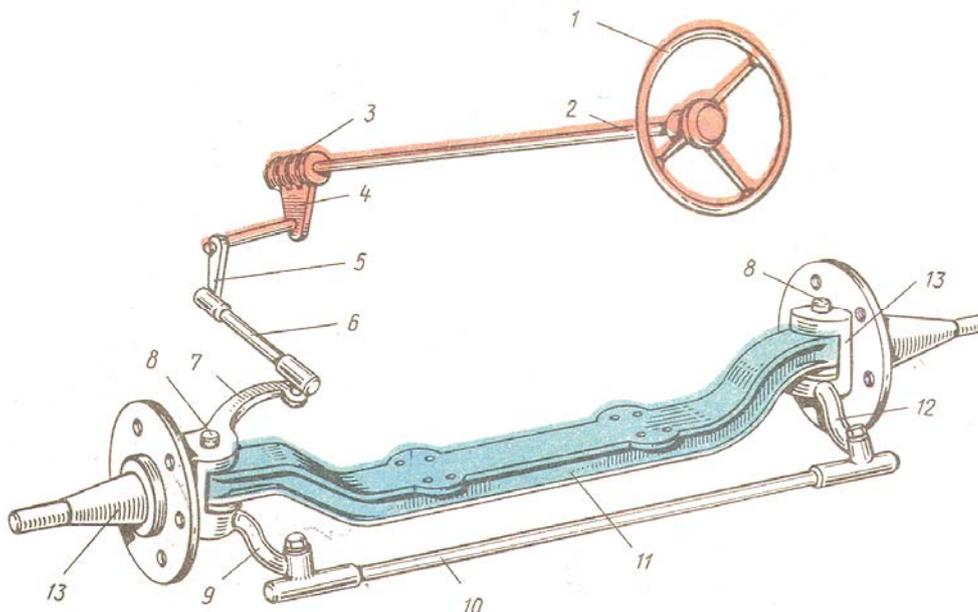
Схема рулевого управления: 1 – рулевое колесо; 2 – вал; 3 – червяк; 4 – сектор; 5 – сошка; 6 – продольная тяга; 7 – рычаги; 8 – шкворень; 9 и 12 – рычаги; 10 – поперечная тяга; 11 – балка; 13 – цапф
